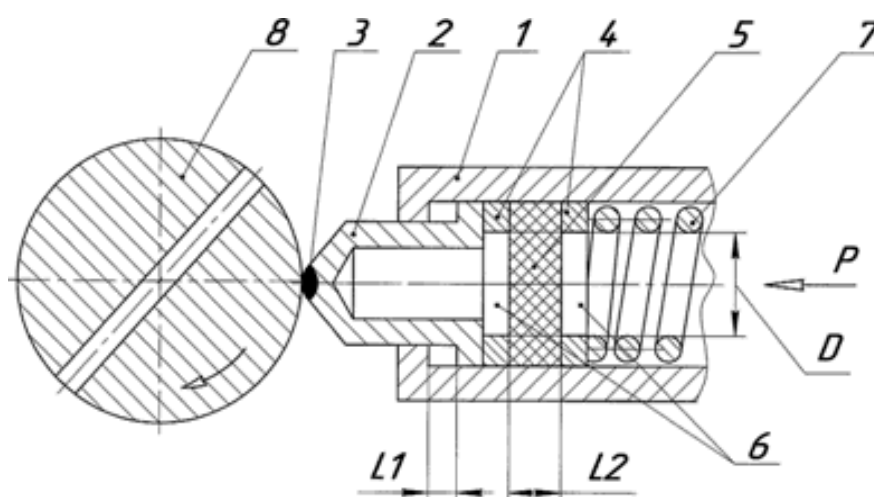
Інструмент для вигладжування переривчастих поверхонь каналів: 1 - корпус; 2 - порожнистий індентор; 3 - алмазний наконечник; 4 - шайби; 5 - гумова шайба; 6 - отвори в шайбах; 7 - пружина; 8 - оброблювана деталь
